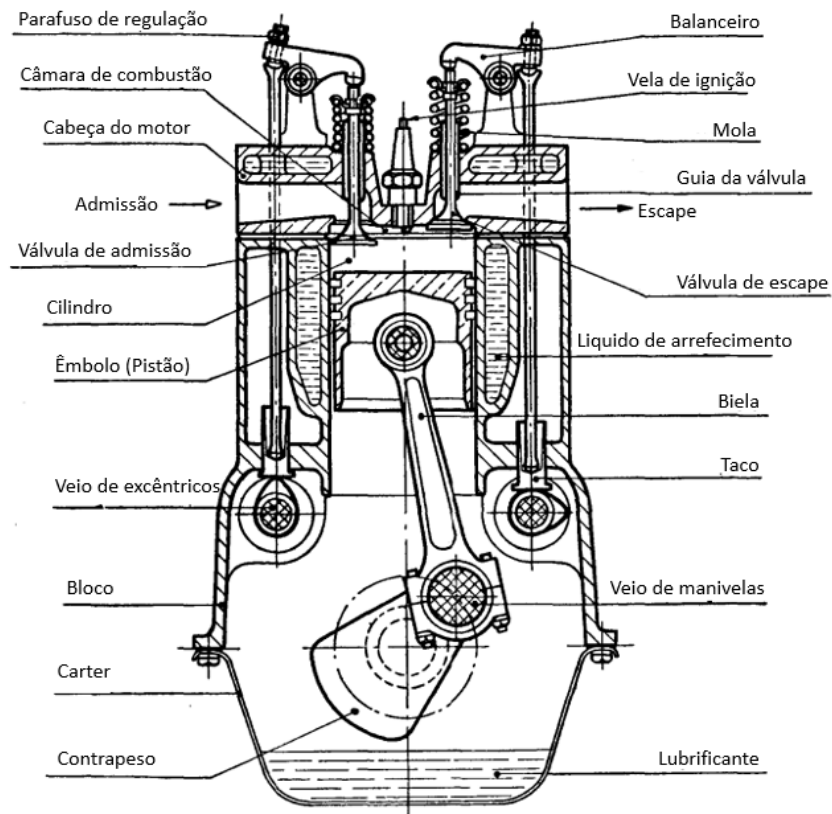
Esquema dos principais componentes do motor alternativo (adaptado de [4])
